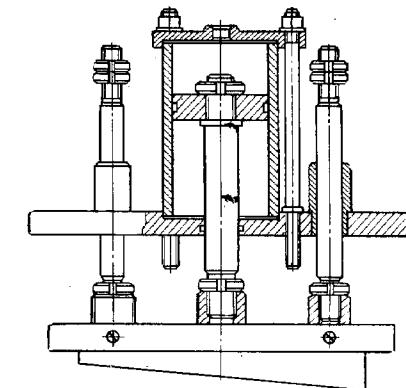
Нажимная часть пневматического стендса для запрессовки стекол дверей в обойму
